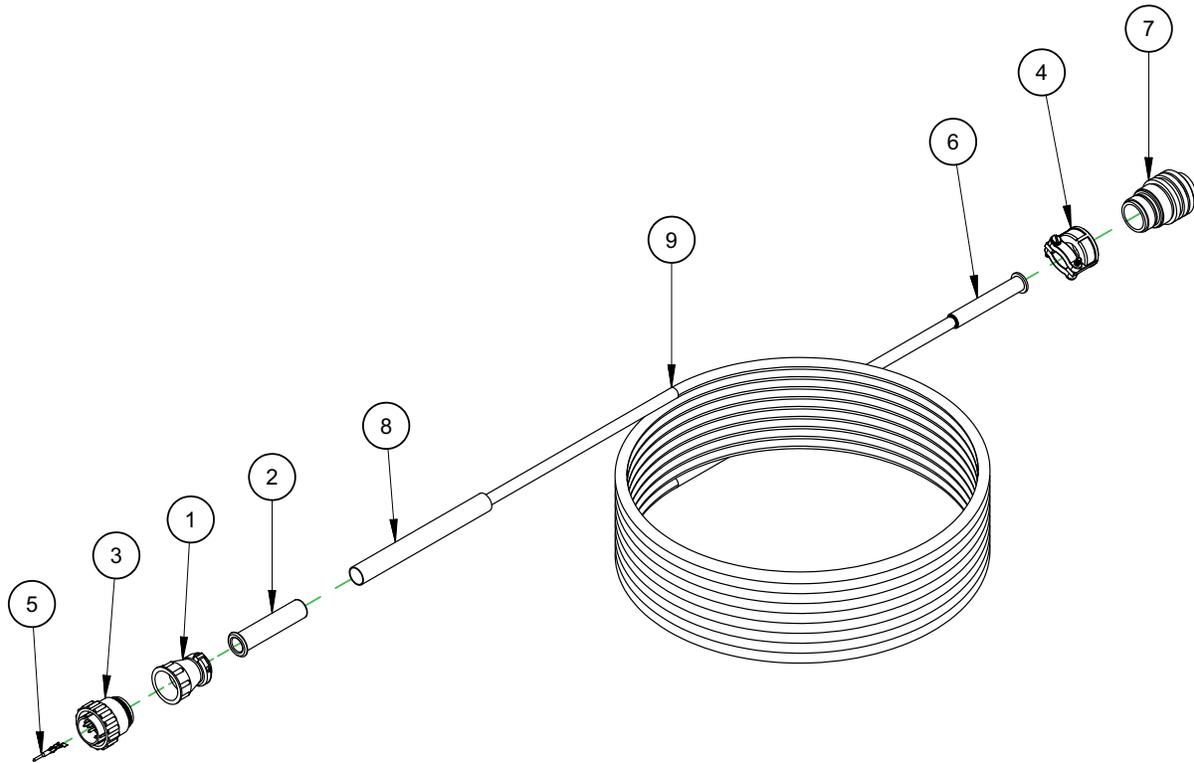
ENSEMBLE SUPPORT ÉLECTRODE (RÉF. 36169)
